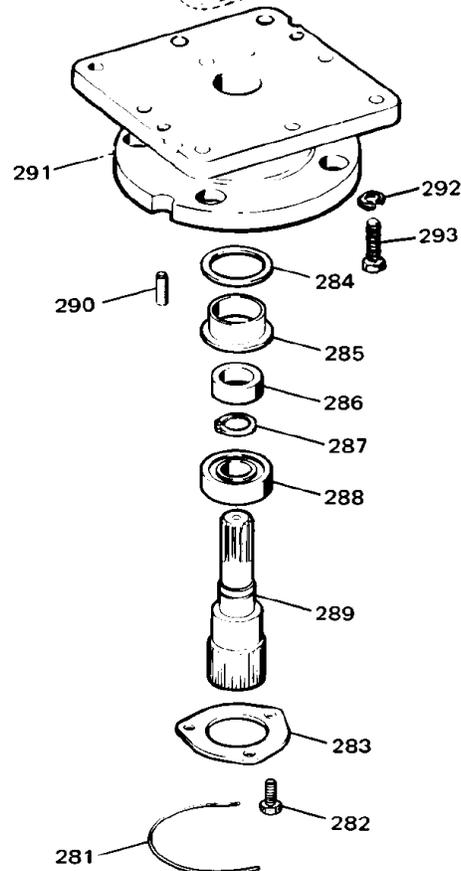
Vista Detalhada, Conjunto Base PG Standard
